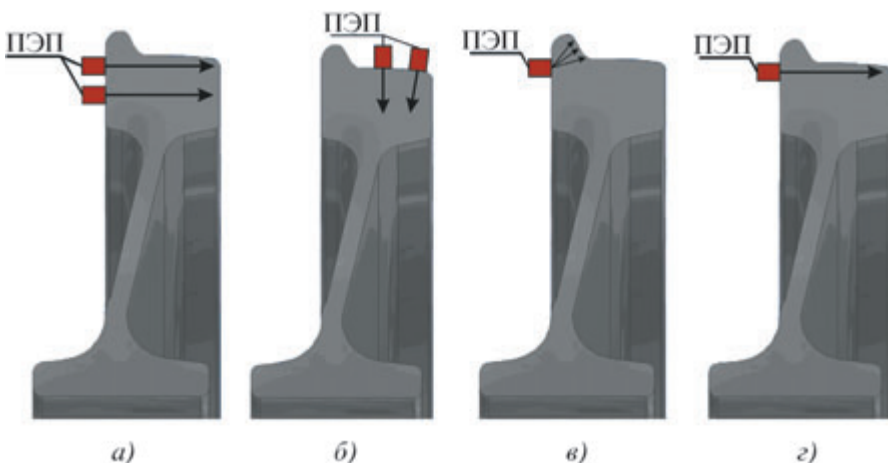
Схемы прозвучивания и зоны контроля цельнокатаного колеса: а – DR2.1, DR2.2; б – DR1.1, DR1.2; в – DR3.1; г – DR3.3
